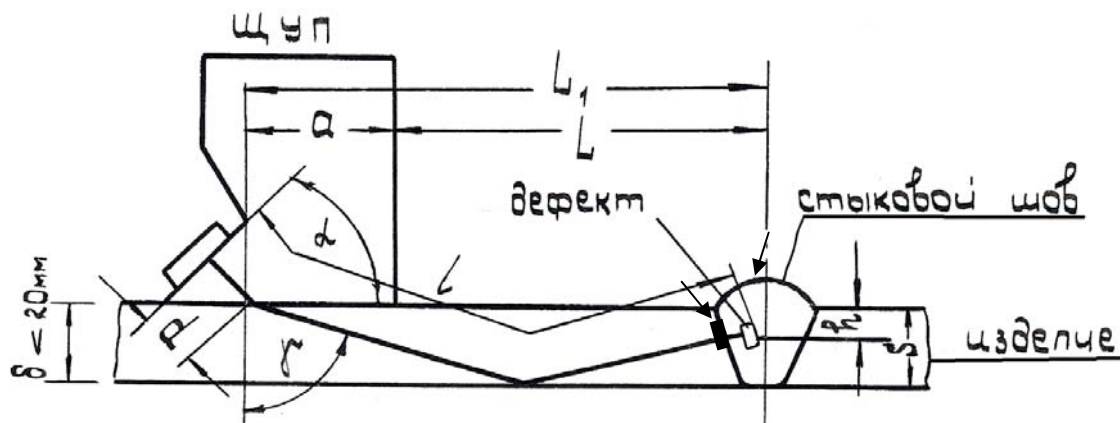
Схема прозвучивания сварного шва однократно отраженным лучом
